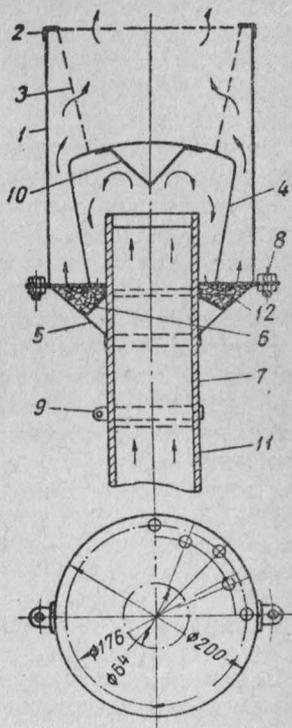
Искрогаситель конструкции Зубаченко для тракторов:
